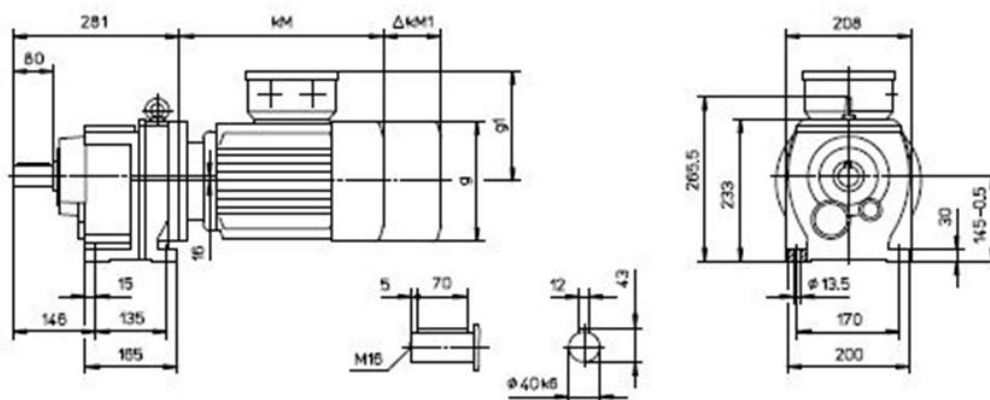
Габаритные и присоединительные размеры мотор – редуктора G93G42A DM90S4
